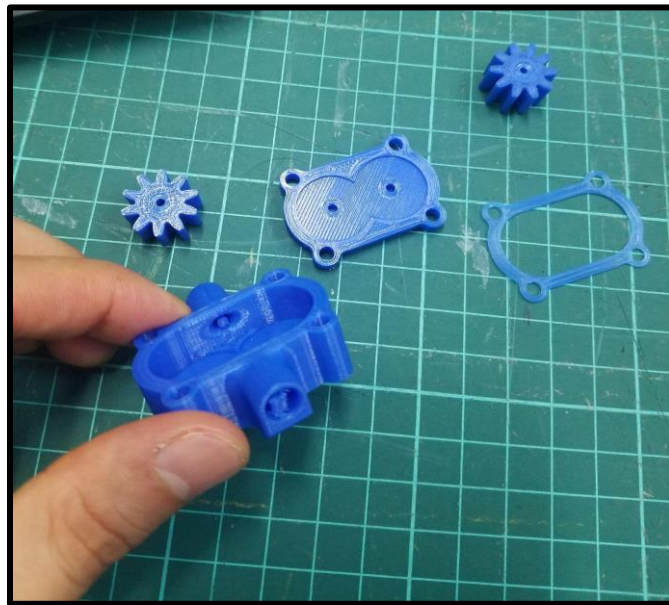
Elementos de la bomba de engranaje previo al ensamblaje
